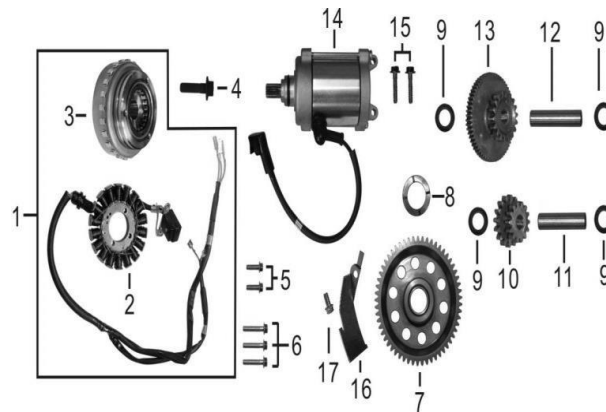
ARRANQUE Y PLATO DE BOBINAS
